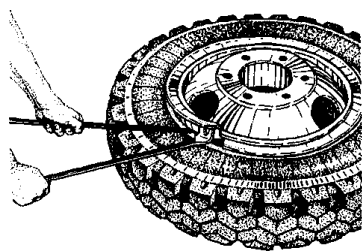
Извлечение бортового кольца из замочной канавки обода
